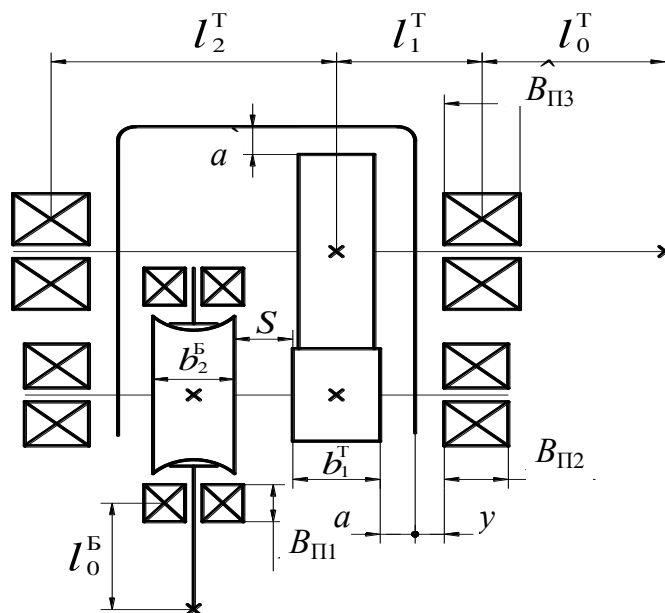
Расчетная схема редуктора (горизонтальный разрез в плоскости разъема крышки и корпуса)
